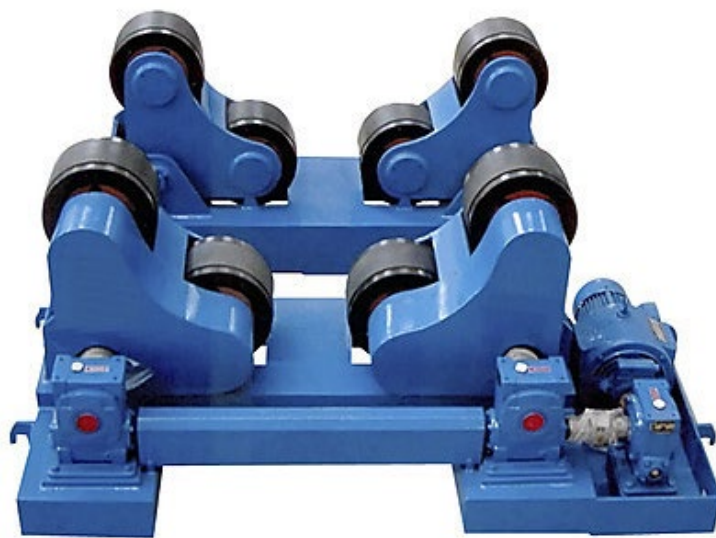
2Самоцентрувальний зварювальний обертач серії HGZ–5
